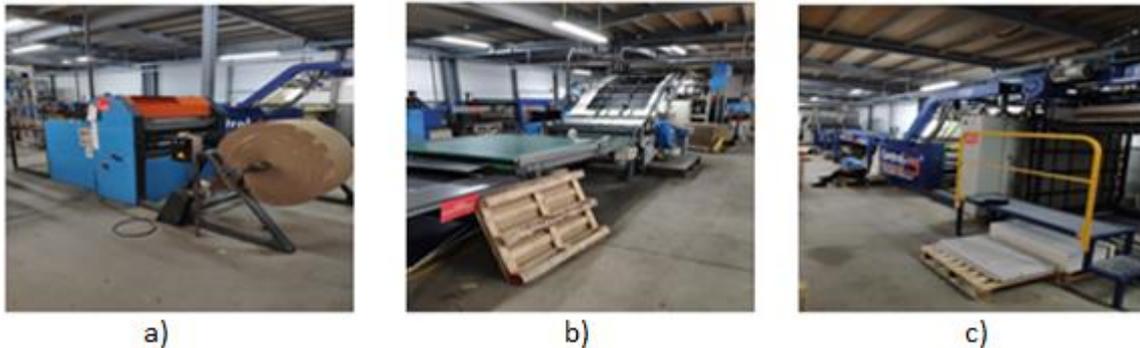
a) Máquina de Corte de Micro; b) Máquina Control 2; c) Máquina Control 3
